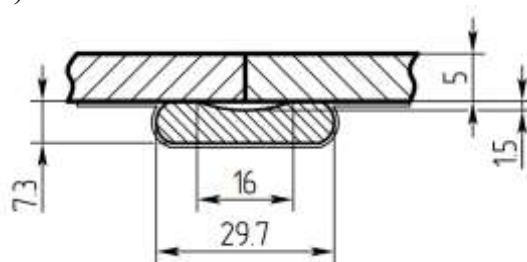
Собранный под сварку образец с приклеенной керамической подкладкой:
